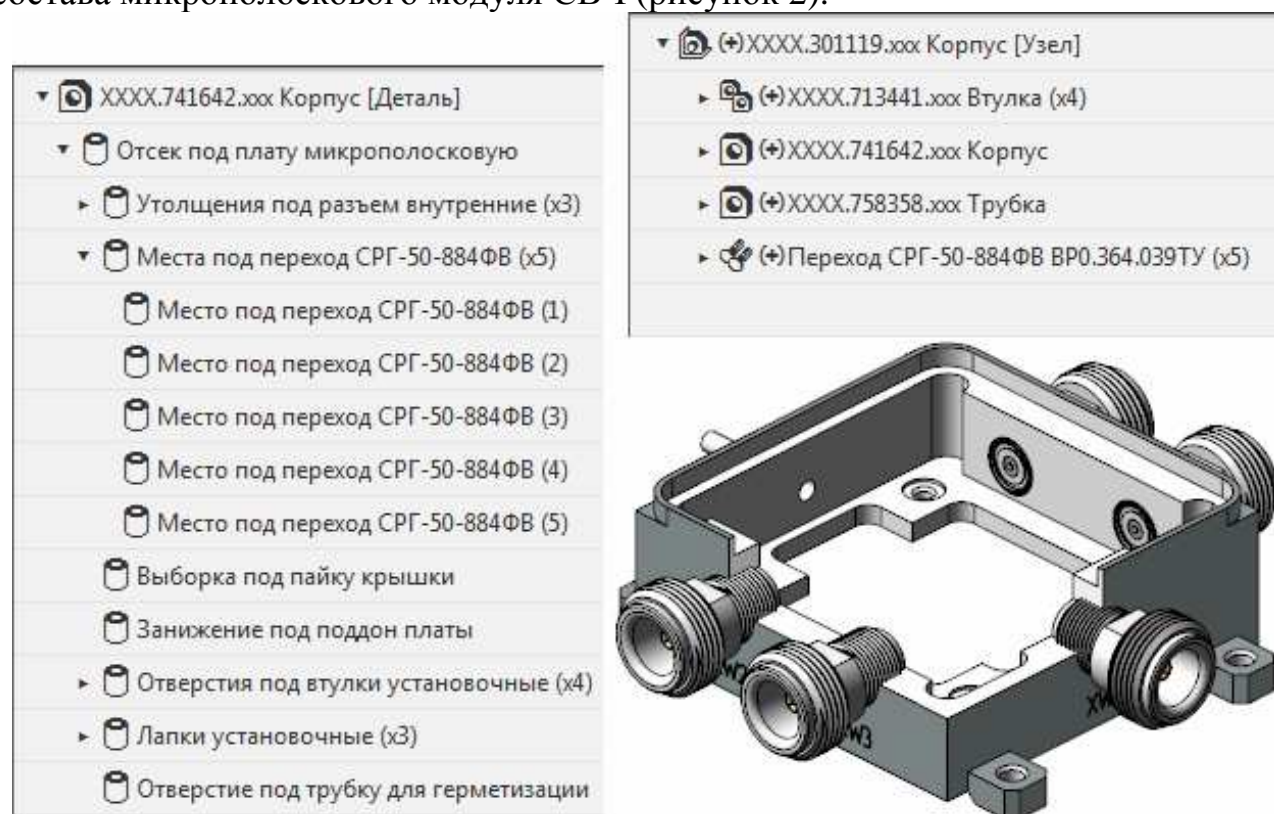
Сборочная 3D-модель узла «Корпус» и дерево построения компонента – детали «Корпус» до модификации
